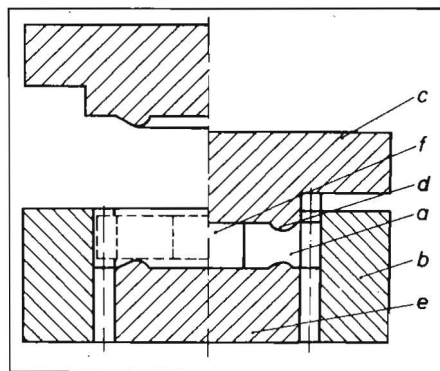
Werkzeug mit Druckwulstelement; a Einzelteil, b Matrize, c Stempel, d Druckwulstelement, e Auswerfer, f Dorn
